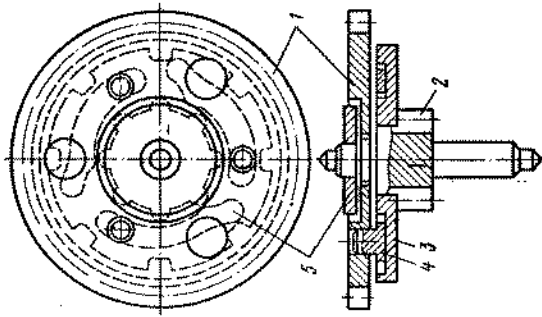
Схема устройства муфты свободного хода часов с автоматическим подзаводом пружиной: 1 — колесо реверсивное; 2 — триб реверсивного колеса; 3 — чашка реверсивной муфты; 4 — собачка; 5 — шайба
